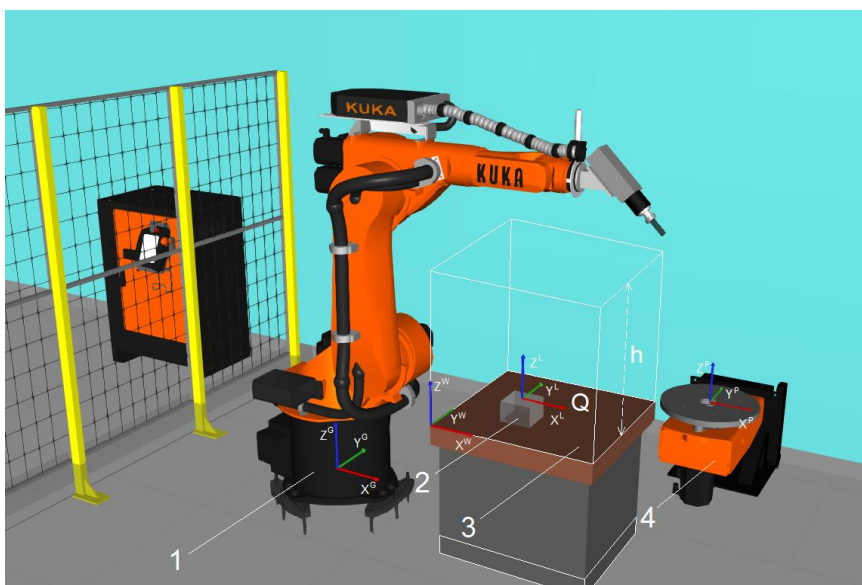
Виртуальная модель РТК механической обработки: 1 – ПР; 2 – заготовка детали; 3 – рабочий фрезерный стол; 4 – промышленный позиционер
